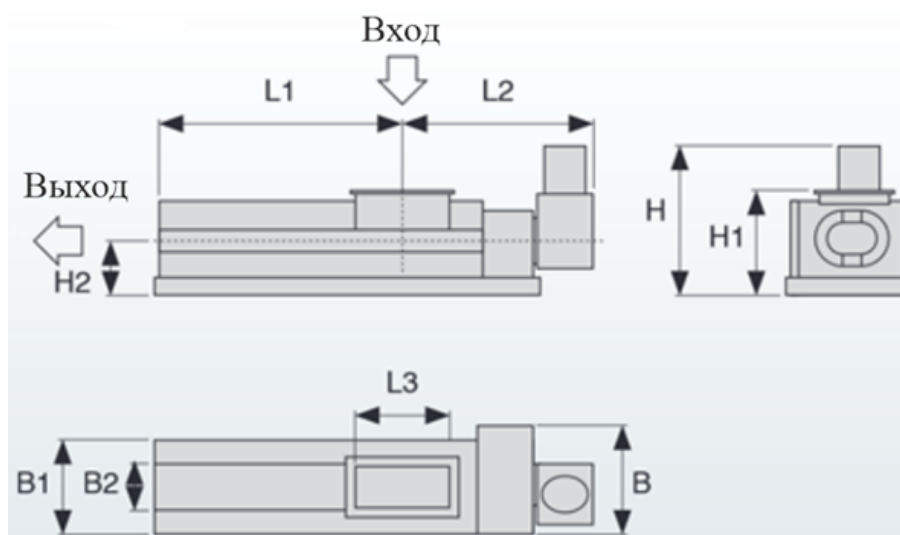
Основные размеры шнекового пресса FAN-beltec ВР 601
